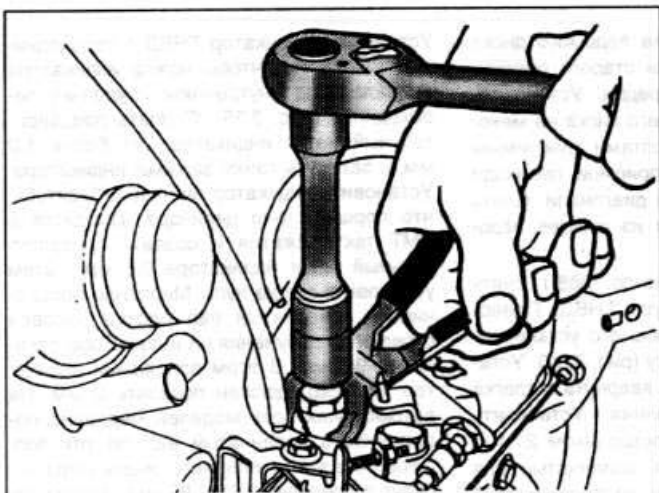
Отвертывание заглушки верхней части корпуса ТНВД на автомобилях выпуска с 1988 г.
